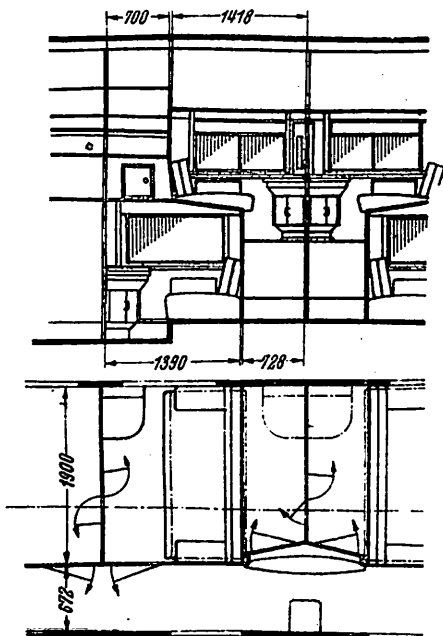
Anderthalbstöckiger Typ mit verschachtelten Querbetten.
